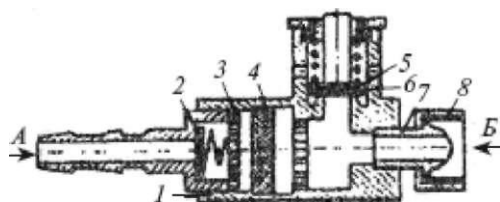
Шланговый обратный клапан: 1 - корпус; 2 - дисковый клапан; 3 - медная сетка; 4 - пористый металлический фильтр; 5 - выпускной клапан; 6 - несгораемый уплотнитель; 7 - ниппель; 8 - накидная гайка
